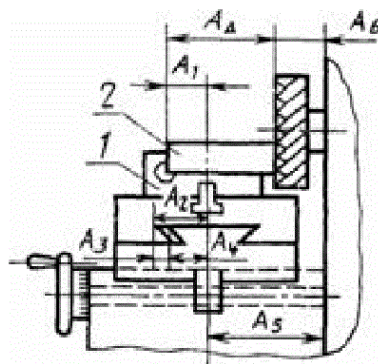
1 - приспособление; 2 - заготовка; A_Δ - размер, полученный в результате обработки
